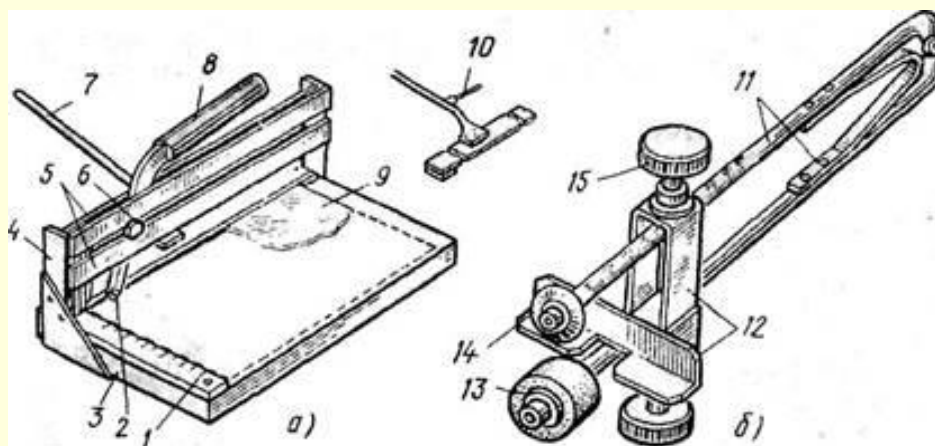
Вигляд роликового (б) плиткоріза важеля (а) для керамічної плитки: наполеглива планка-лінійка, 2, 14-роликові раці, 3- підстава, 4 - стійка, спрямовуючі, 6-каретка, 7-ручка притиску, 8 - вазки, 9- керамічна плитка, 10-пружина, 11-стрижні з пружиною, 12 - движок, 13 - гумовий вал 15 - затискний гвинт
